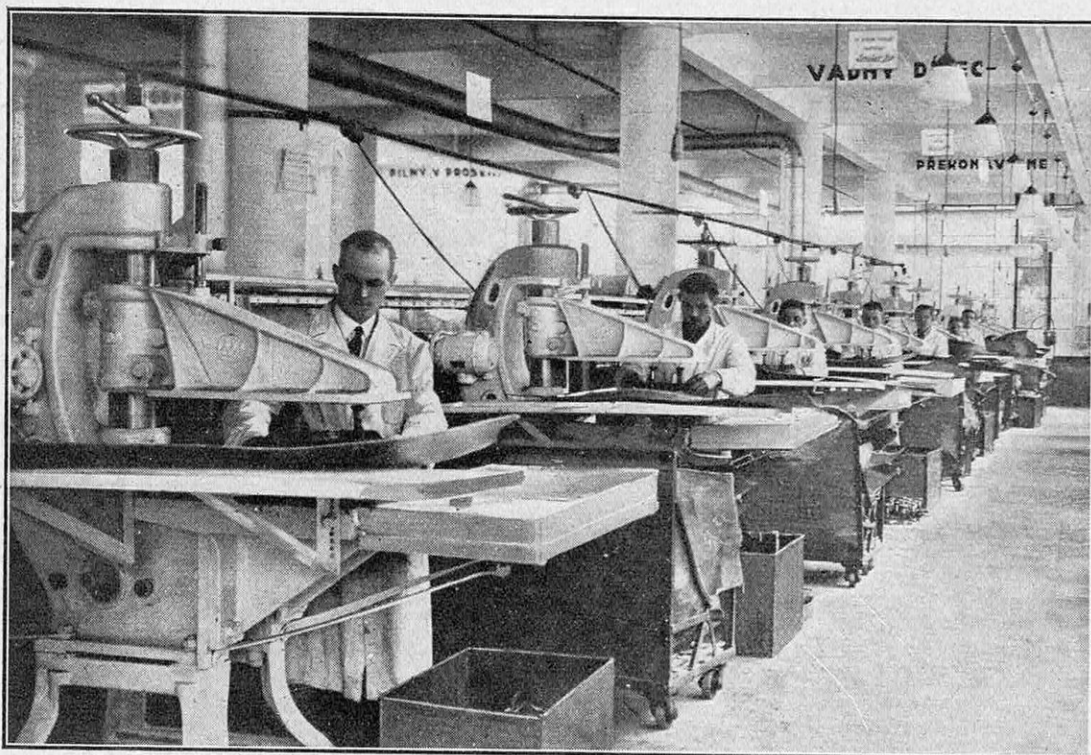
LE DÉCOUPAGE DES SEMELLES A L'EMPORTE-PIÈCE A REMPLACÉ LE DÉCOUPAGE A LA MAIN DANS LES GRANDES USINES DE ZLIN (TCHÉCOSLOVAQUIE)
